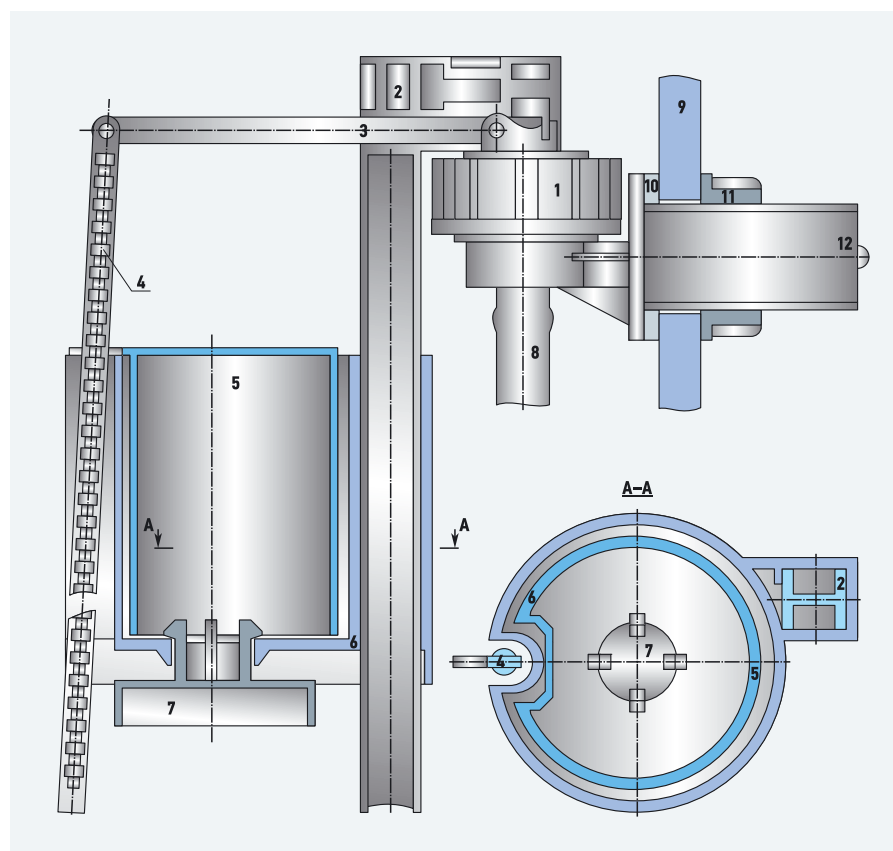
Конструктивная схема наполнительной арматуры с сервоуправлением ЗАО «Уклад» (1 — головка наполнительной арматуры; 2 — кронштейн; 3 — рычаг; 4 — тяга; 5 — поплавок; 6 — емкость для размещения поплавка; 7 — обратный клапан; 8 — противозумная трубка; 9 — боковая стенка смывного бачка; 10 — уплотнительная прокладка; 11 — крепежная гайка; 12 — фильтр)
